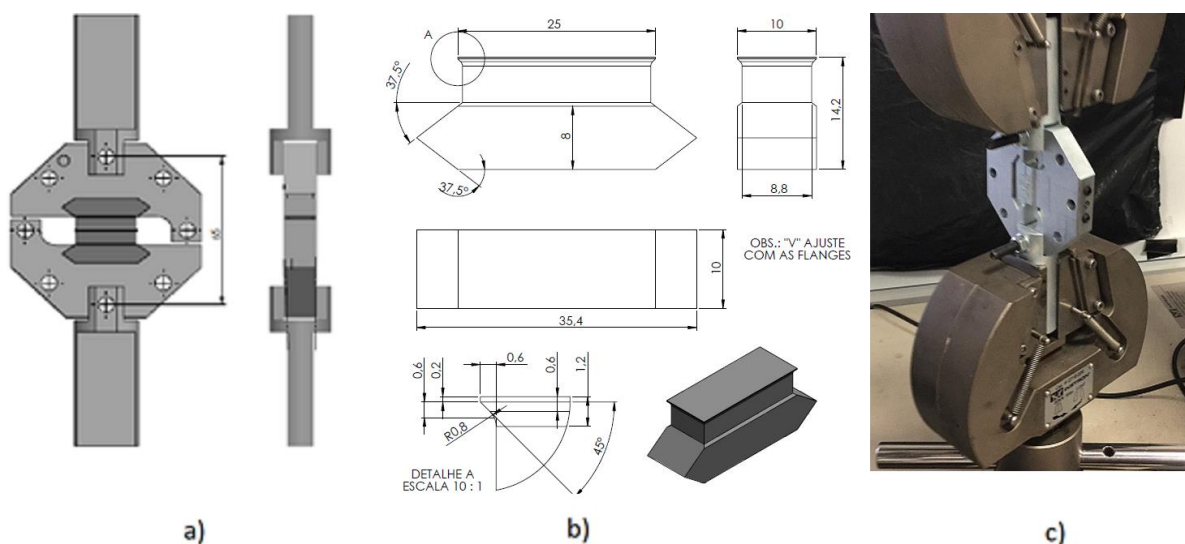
a) Geometria do dispositivo de Arcan reduzido, b) Dimensões do substrato metálico, onde o adesivo foi aplicado, c) Montagem no equipamento. (dimensão em milímetros).
